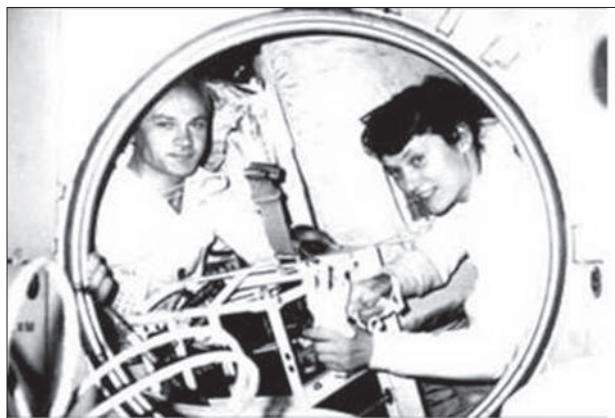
Летчики-космонавты СССР С. Е. Савицкая и В. А. Джанибеков на предполетных испытаниях сварочного инструмента
